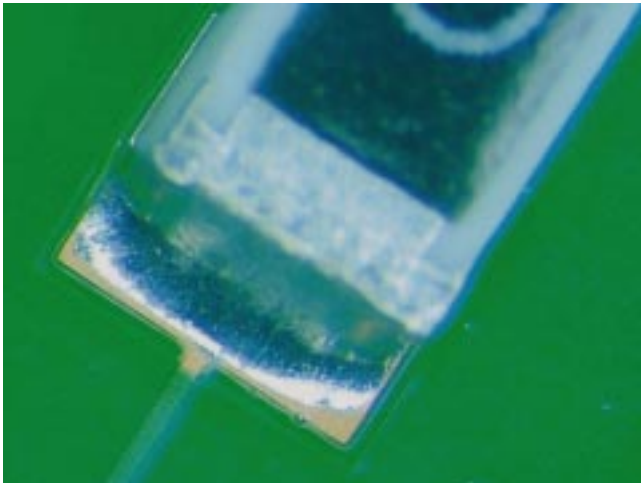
Soldadura SnPb; Proceso No-Lavable
